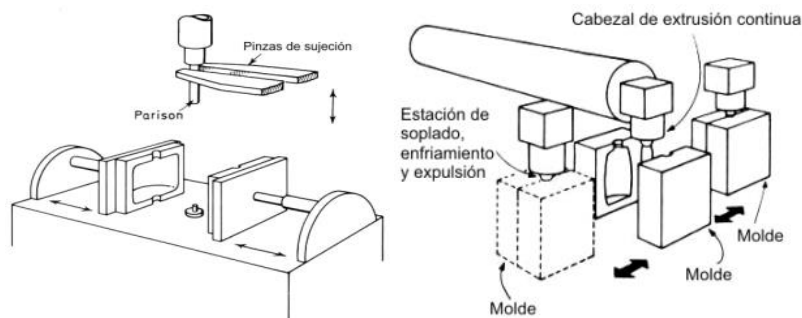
Proceso continuo a) (derecha) Moldes móviles b) (izquierda) Moldes fijos.
